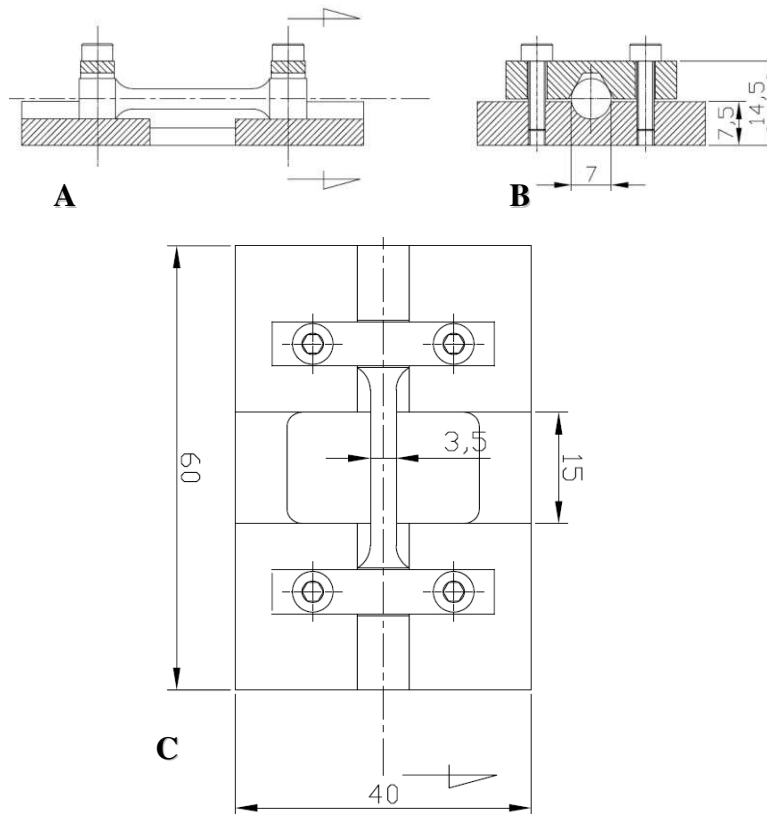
Dispositivo metálico para soldagem com o posicionamento do corpo de prova: (A) Vista frontal; (B) Vista lateral; (C) Vista superior
